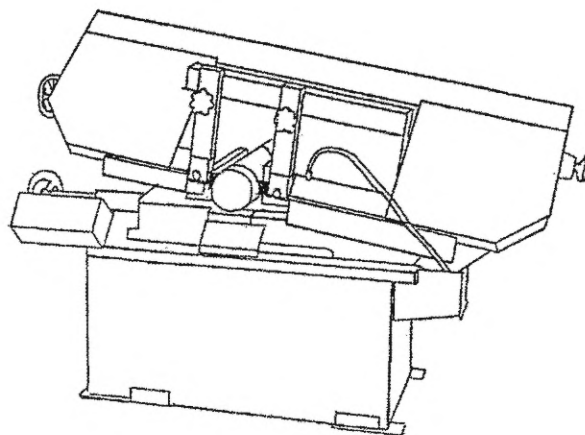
Горизонтальный ленточнопильный станок — поворотный тип
